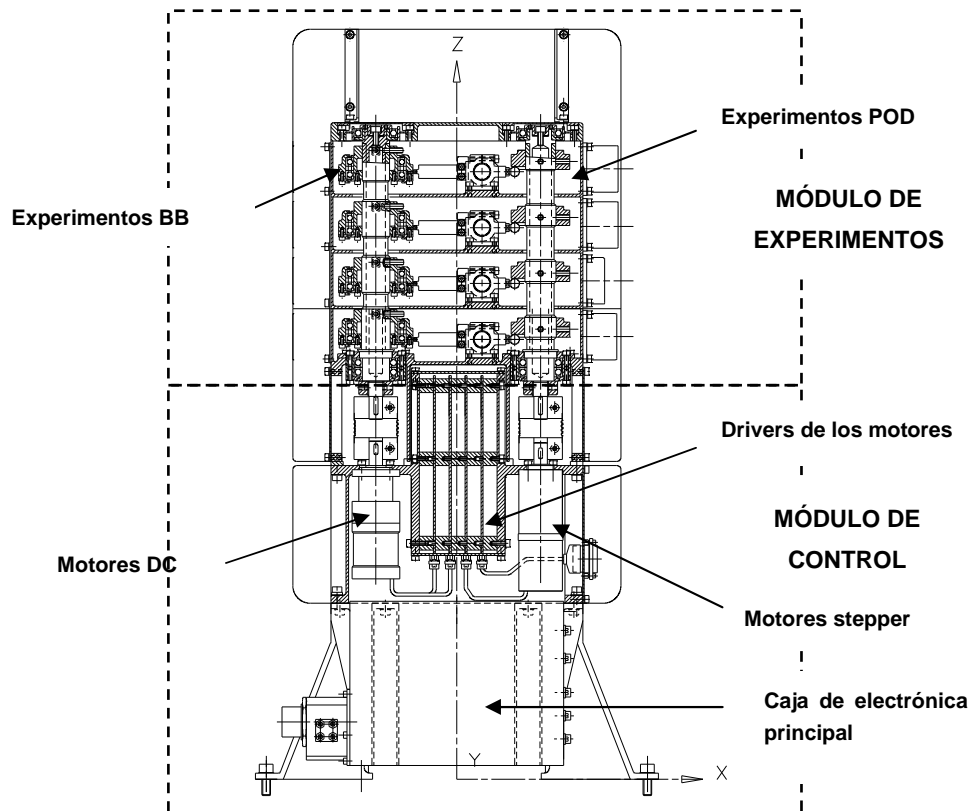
Croquis de la configuración estructural del TriboLAB.
